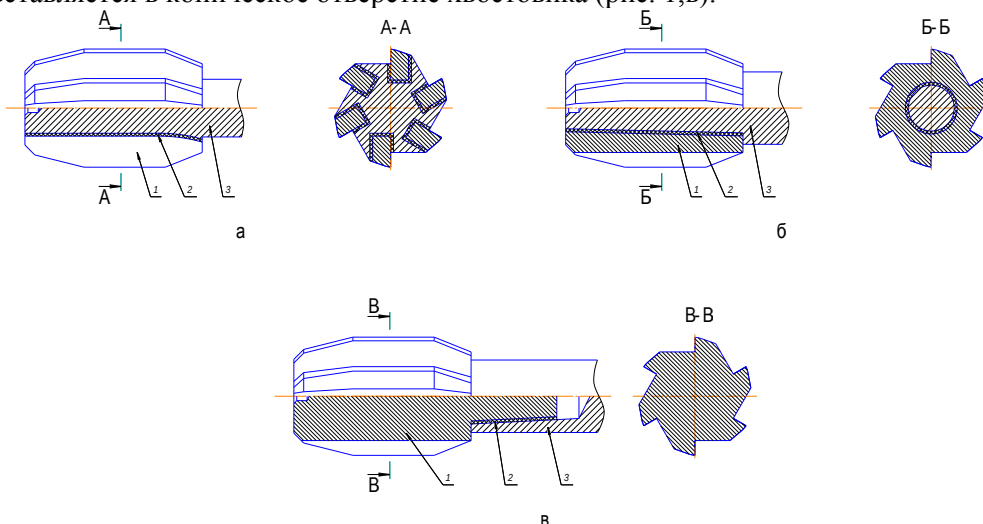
Варианты рабочей части разверток с твердосплавными элементами в виде пластин (а), втулок (б) и вставок (в):
